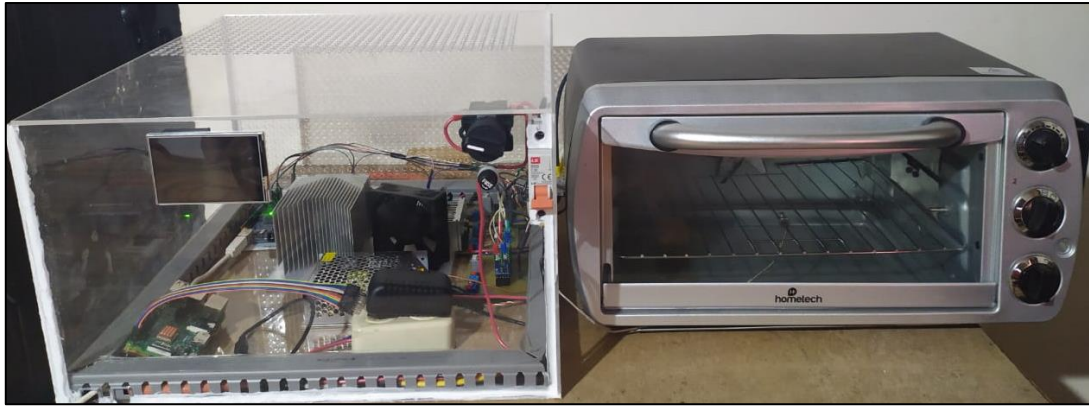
Equipo de soldadura SMD finalizado.
